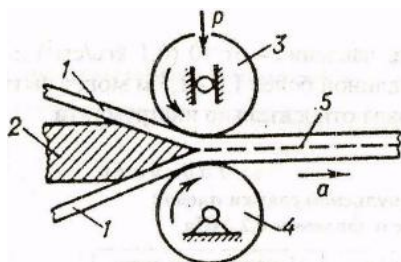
Схема непрерывной сварки пленок внахлест при нагреве инструментом соединяемых поверхностей:
